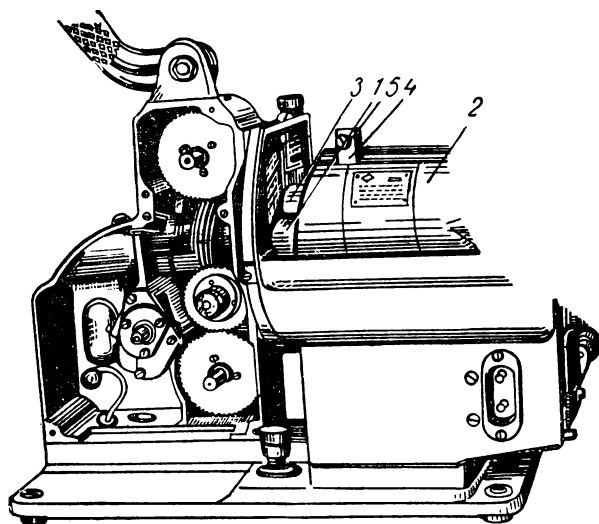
Устройство регулировки фрикционного сцепления ведущего шкива электродвигателя с ведомым шкивом головки кинопроектора (маховик стабилизатора и крышки головки и фонаря кинопроектора сняты): 1 — ведущий шкив; 2 — электродвигатель; 3 — ведомый шкив; 4 — прилив на электродвигателе; 5 — регулировочный винт
